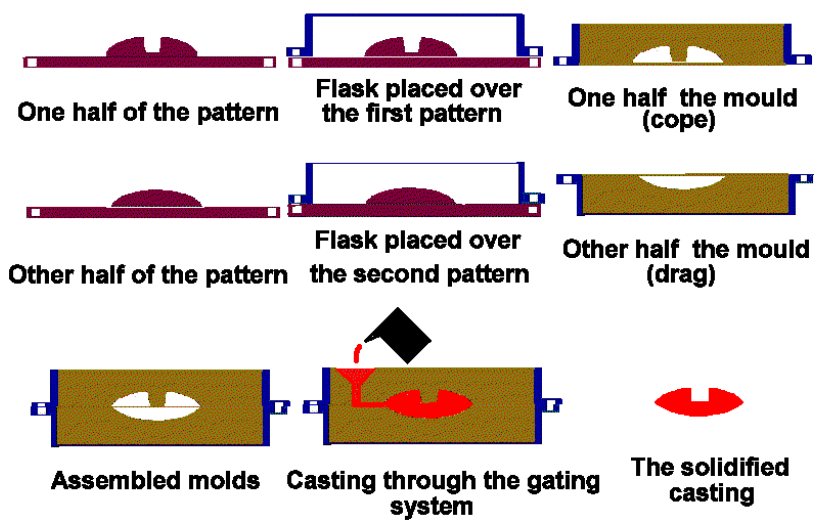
Procés d'emmotlament en motlles de sorra
